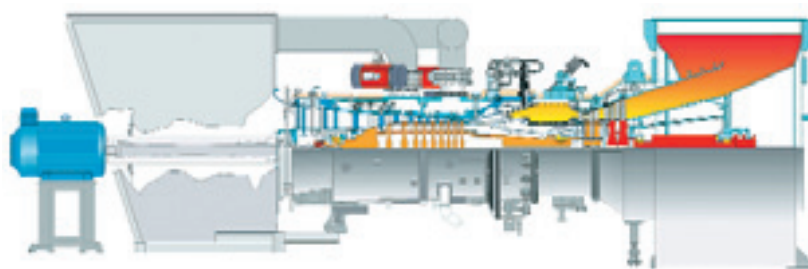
Конструкция газотурбинного агрегата SGT-600
